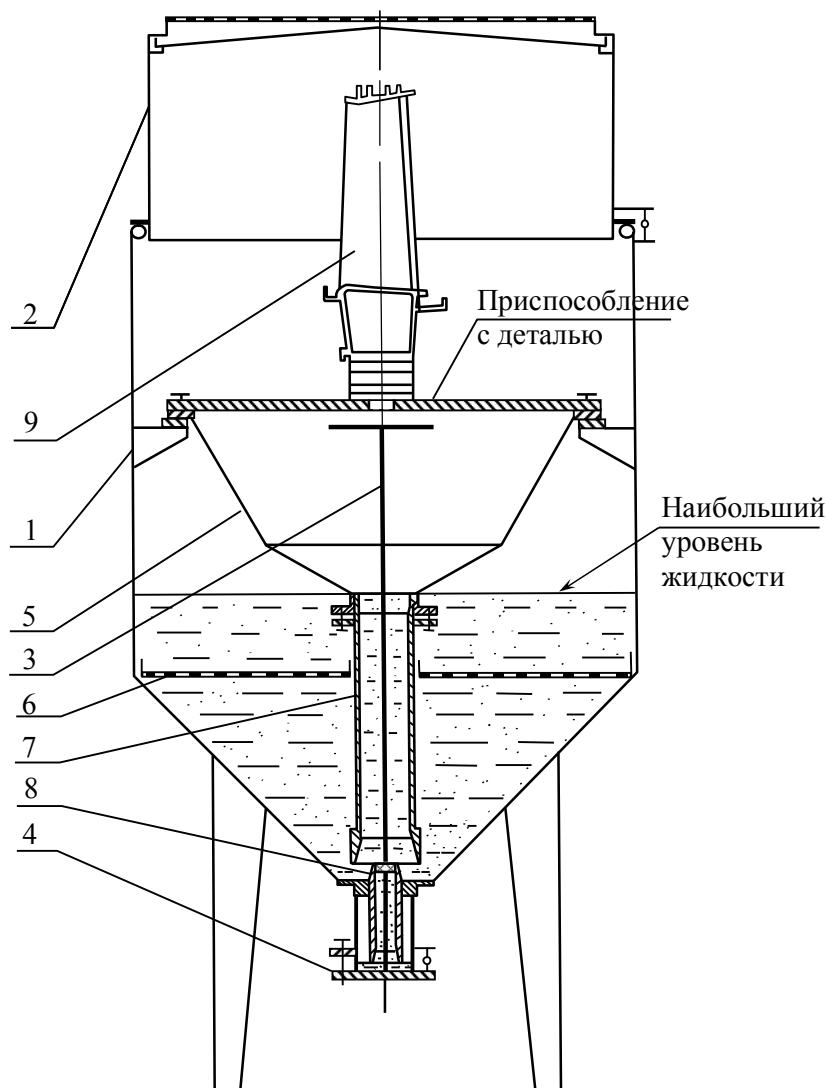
Установка для абразивной очистки внутренних поверхностей деталей:
